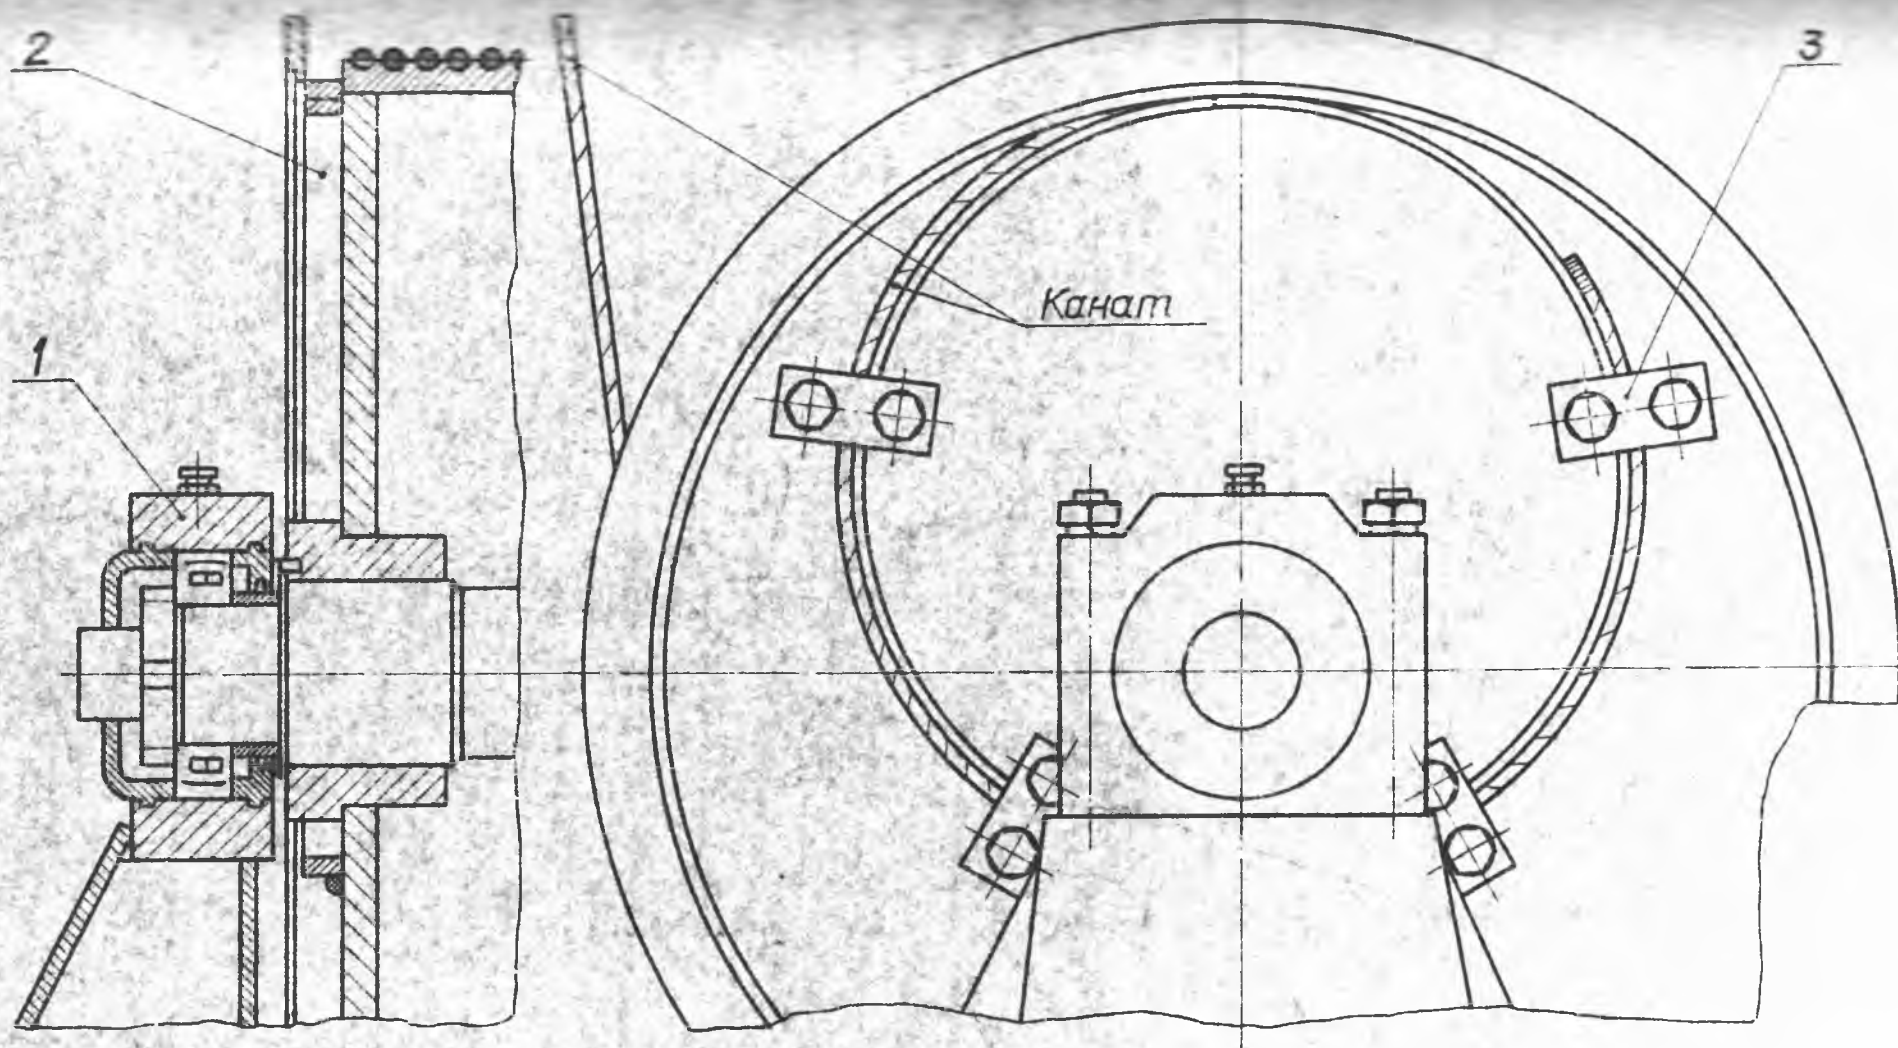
Опора барабана в коренном подшипнике и крепление каната на барабане.
